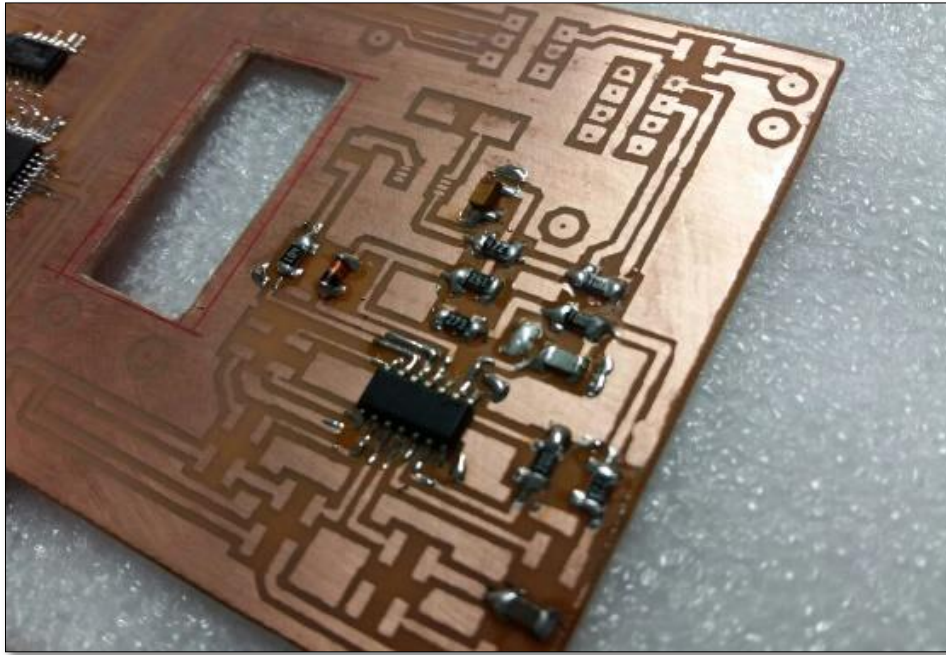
Suelda de elementos en la placa del regulador de voltaje
